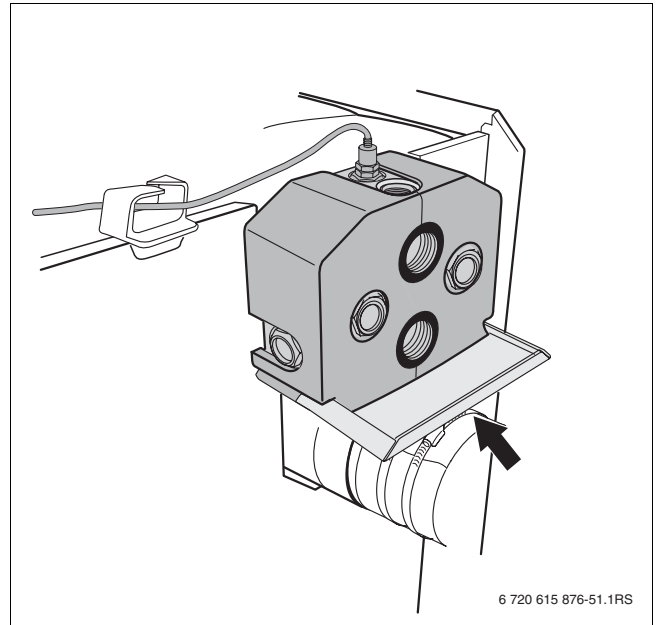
Montaggio della lamiera di protezione da irraggiamento
